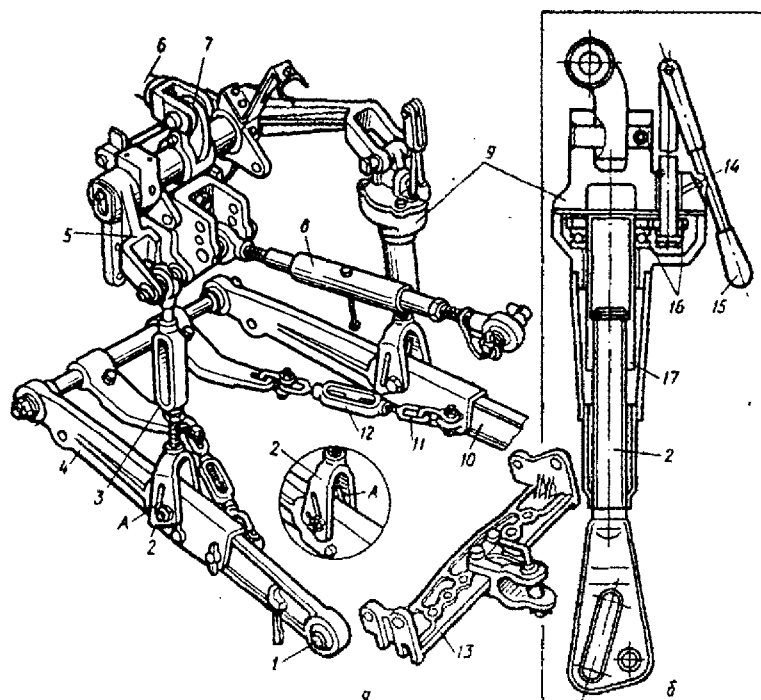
Заднее навесное устройство универсально-пропашных тракторов: а – устройство; 6 – регулировочный раскос; 1 – сферический (шаровой) шарнир; 2 – вилка раскоса; 3 – левый раскос; 4 – продольная тяга; 5 – подъемный рычаг; 6 – шток цилиндра; 7 – поворотный рычаг; 8 – верхняя центральная тяга; 9 – редуктор правого раскоса; 10 – удлинитель; 11 – ограничительная цепь; 12 – стяжка цепи; 13 – прицепное устройство; 14 – масленка; 15 – рукоятка; 16 – шестерни; 17 – труба раскоса
